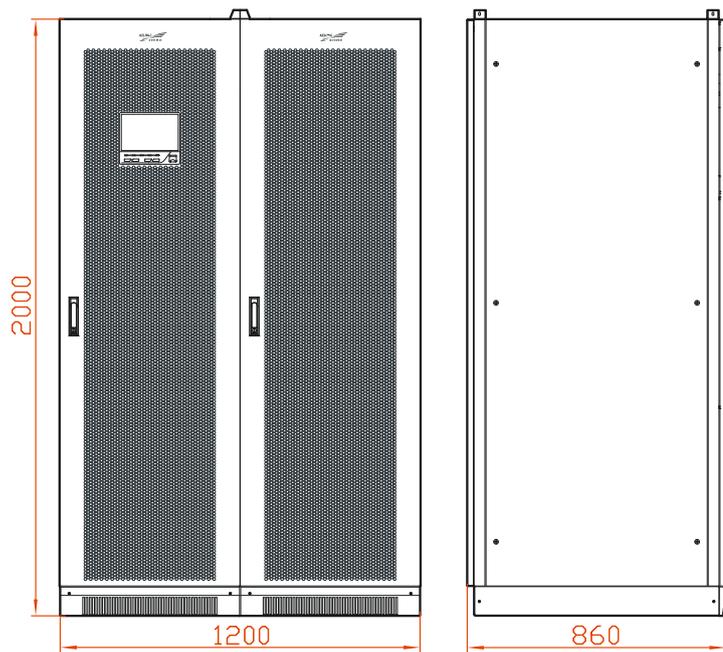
Размер для MR33400, MR33500, MR33600
